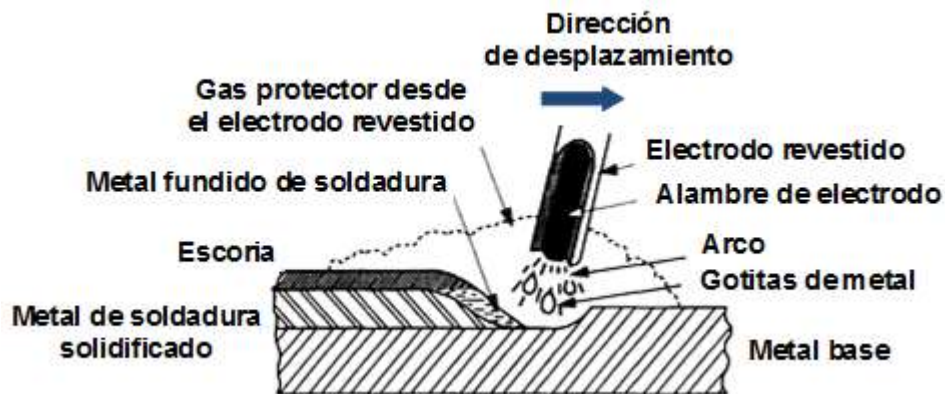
Proceso de Soldadura por arco metálico [5].
